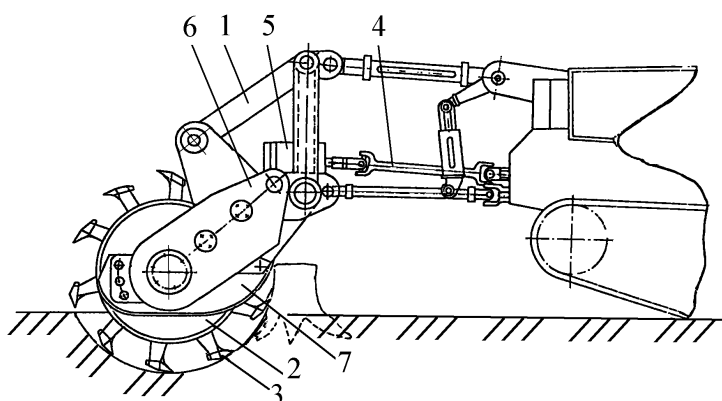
Машина для подготовки почвы и дробления пней МДП-1,5: 1 – рама; 2 – рабочий орган; 3 – скалывающие ножи; 4 – карданный вал; 5 – конический редуктор; 6 – цилиндрический редуктор; 7 – опорные лыжи
